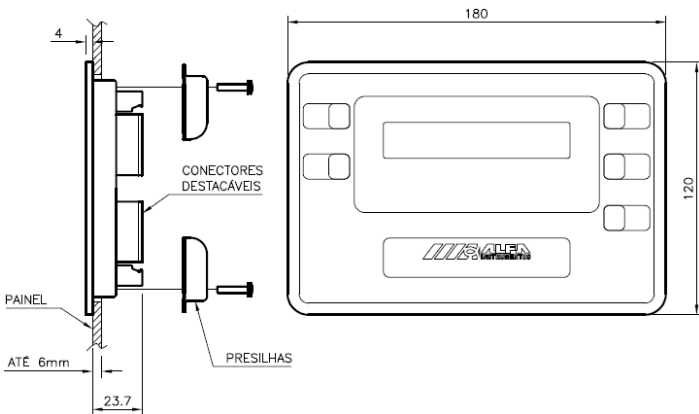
Linha 3100C.S dimensões do Indicador de Pesagem
